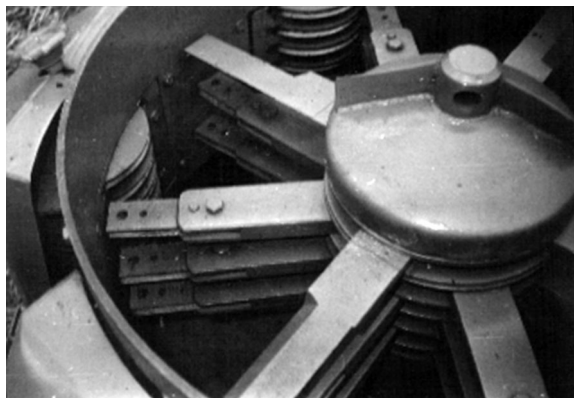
Измельчитель с установленными в державке двумя режущими ножами
